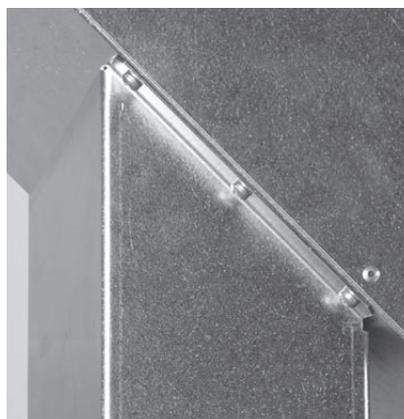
Fissare il piede d'appoggio con 3 viti su ciascun lato
